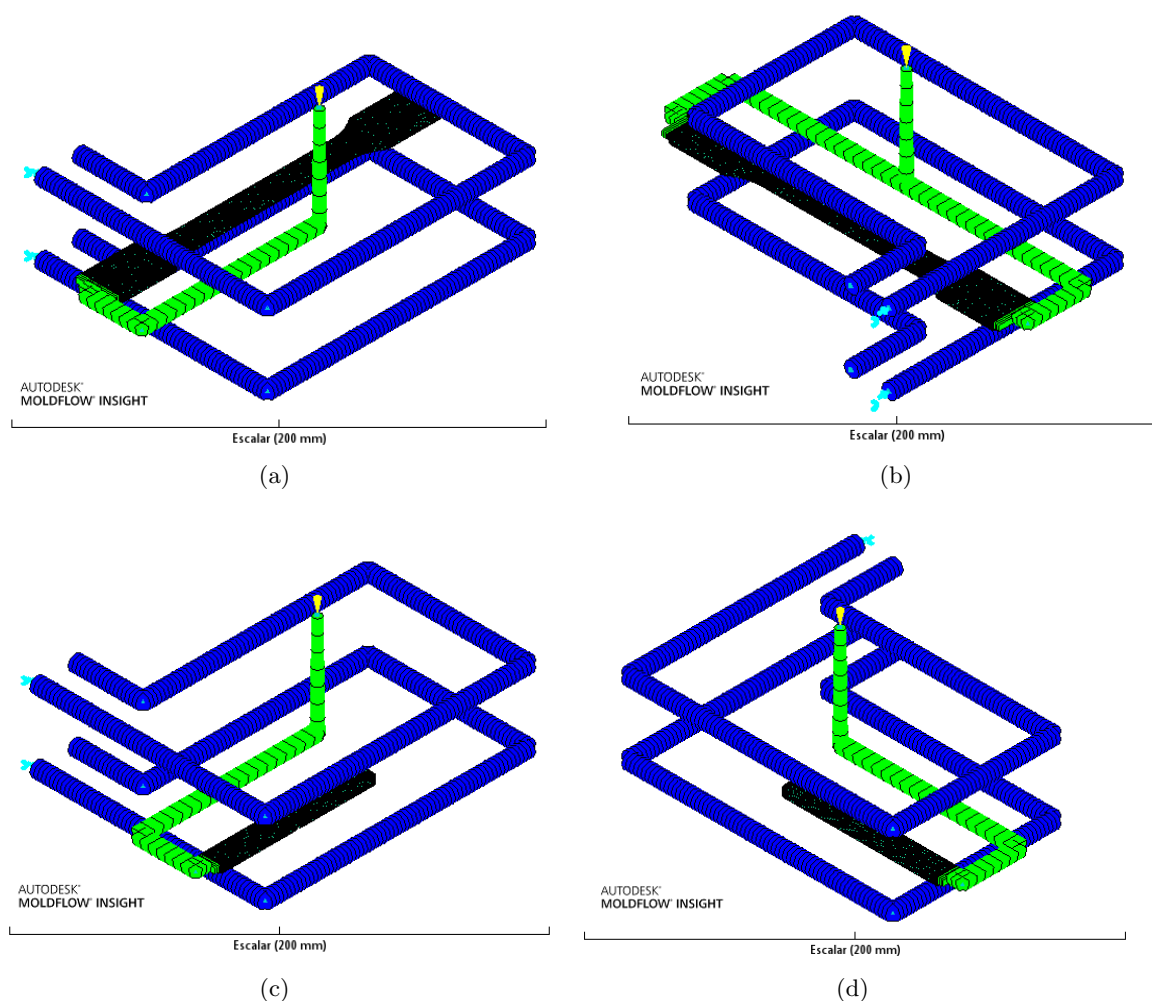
Modelo geométrico para análise do provete de: (a) tração, (b) tração com linha de soldadura, (c) impacto com entalhe e d) impacto sem entalhe ou flexão.
